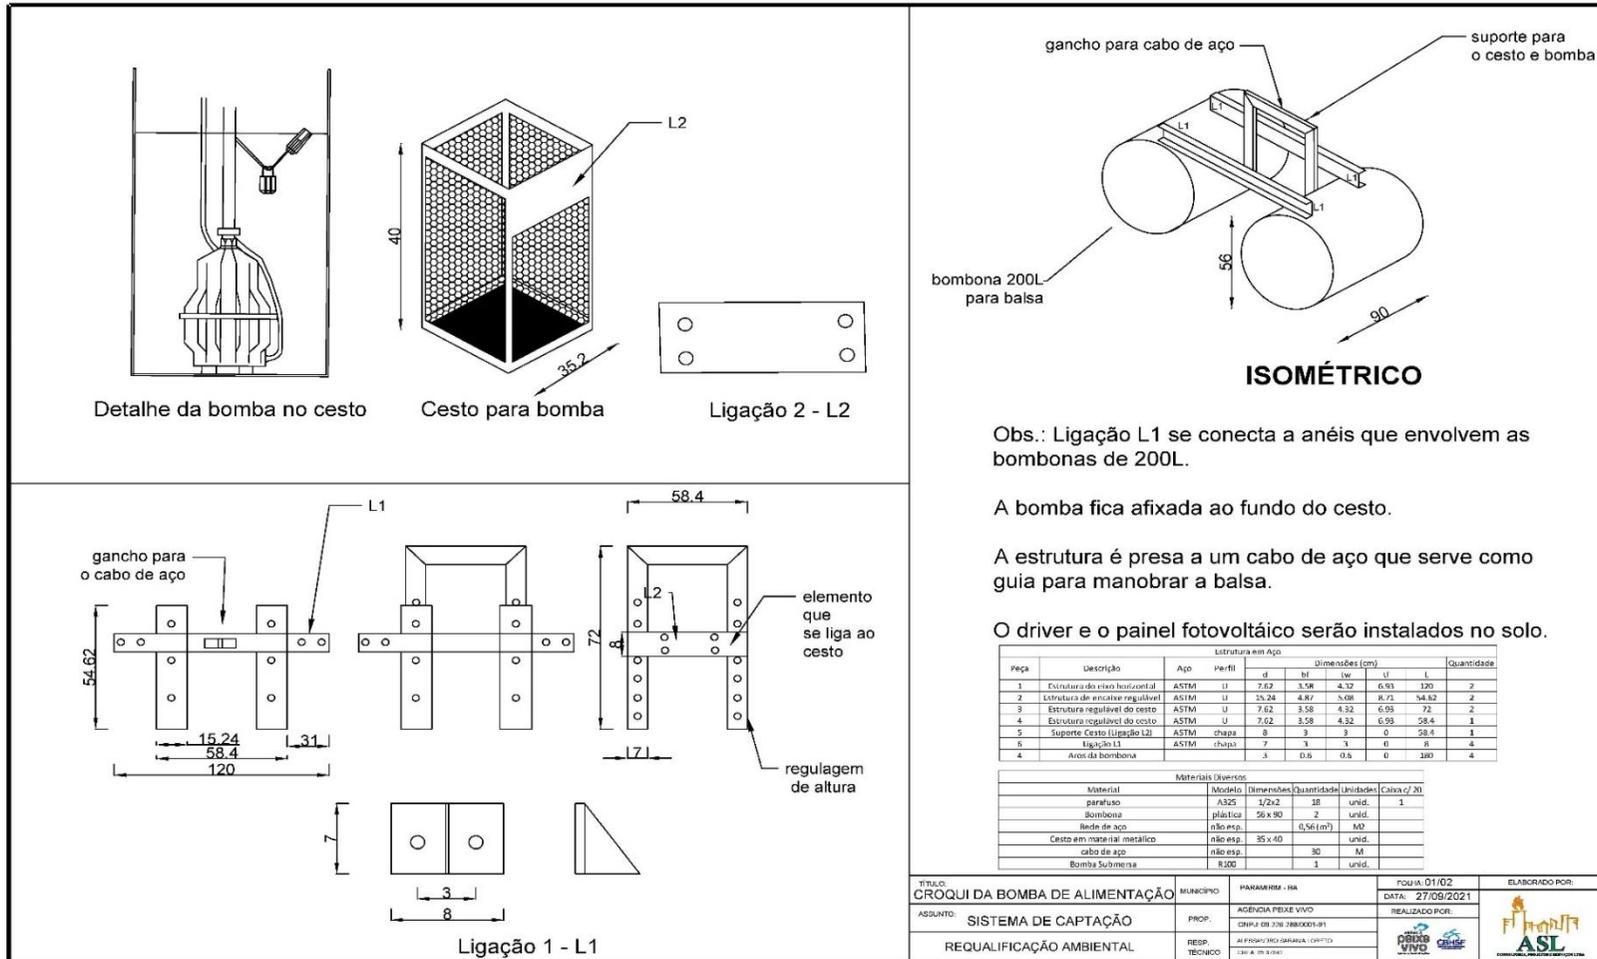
Croqui da balsa flutuante de captação para abastecimento do bebedouro
